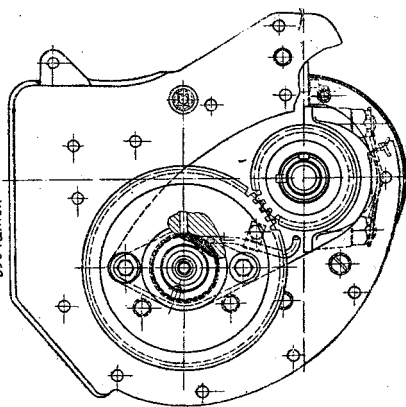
Поперечный разрез шестипоршневого двигателя (вентиляция картера и смазка).
